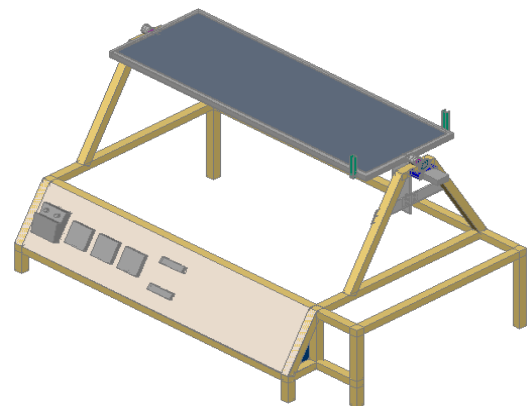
Montaje de la Placa Soporte de Dispositivos
